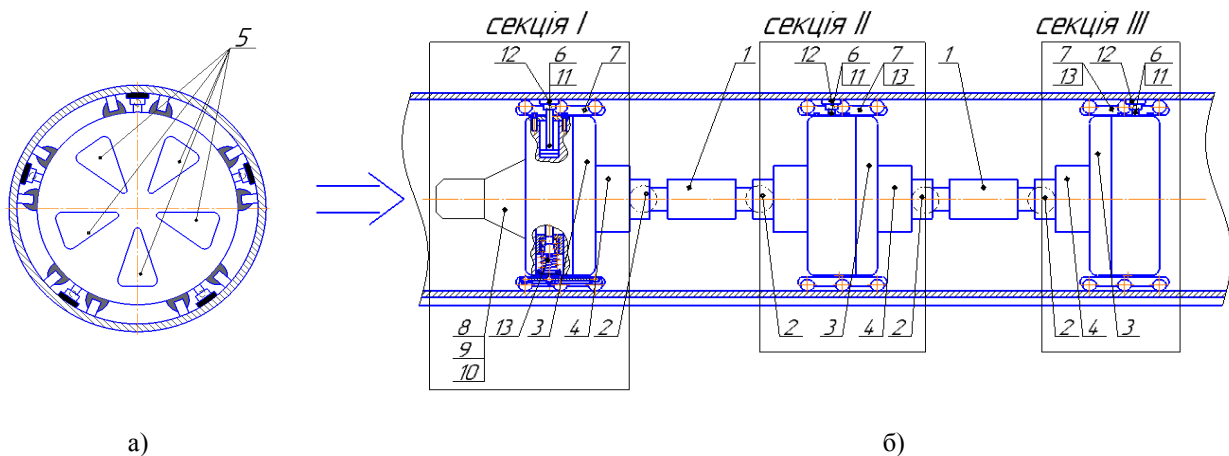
Принципова схема мобільного пристрою: а) вид спереду; б) вид зліва
